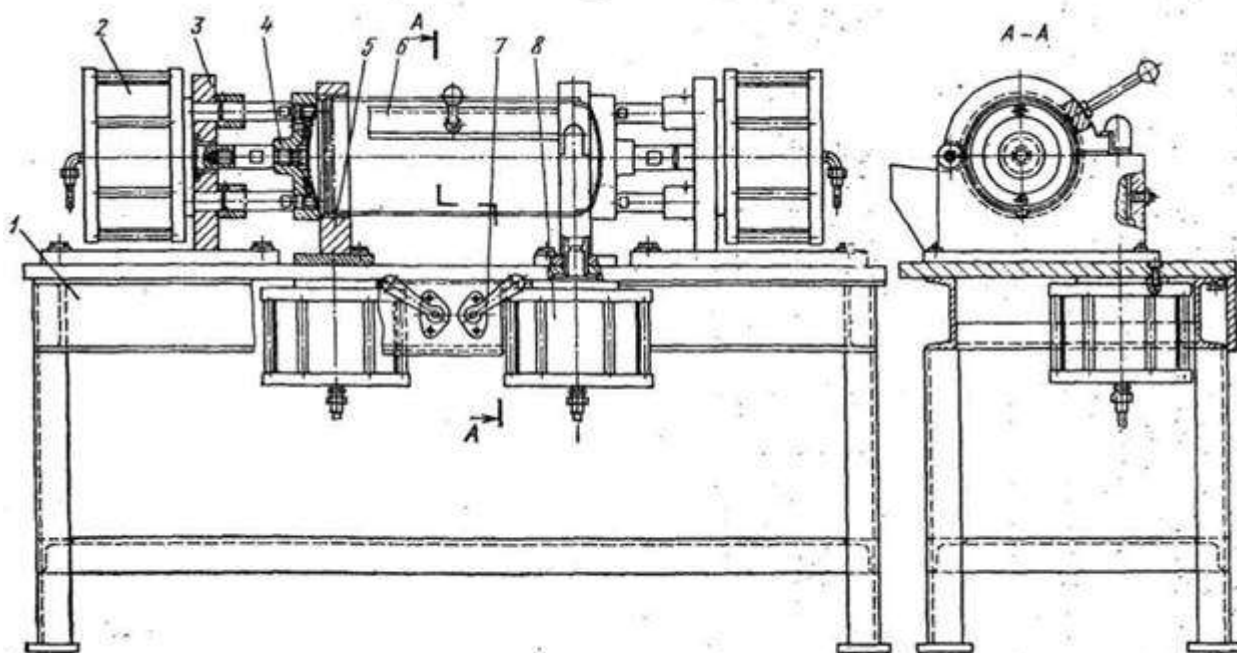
Установка для сборки небольших обечаек с донышками
